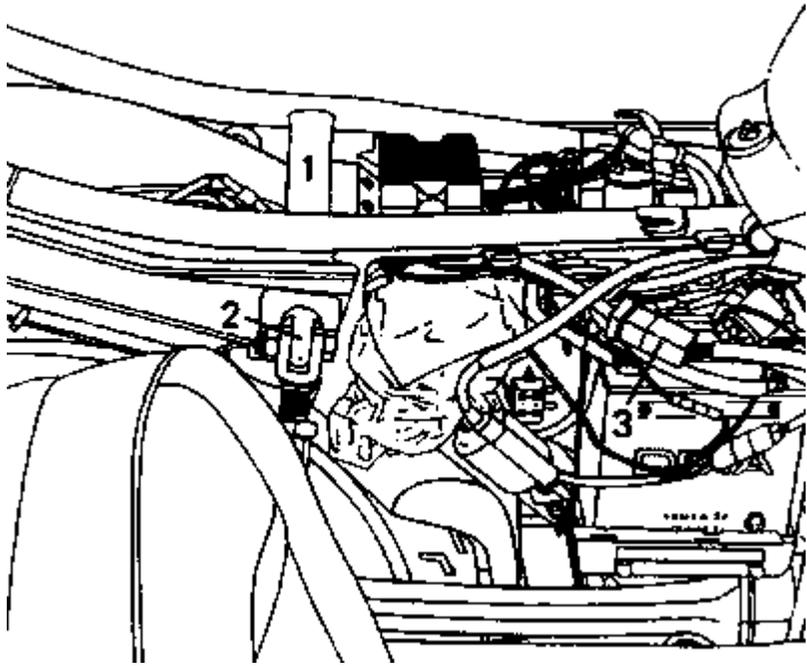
Rahmen des Motorrades für Seitenwagenbetrieb
